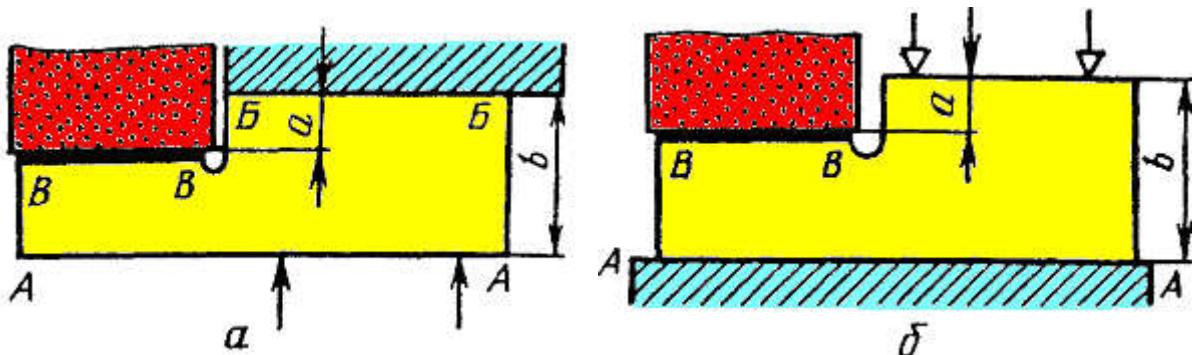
Установка заготовки при плоском шлифовании поверхности ВВ по плоскостям ББ (а) и АА (б)
